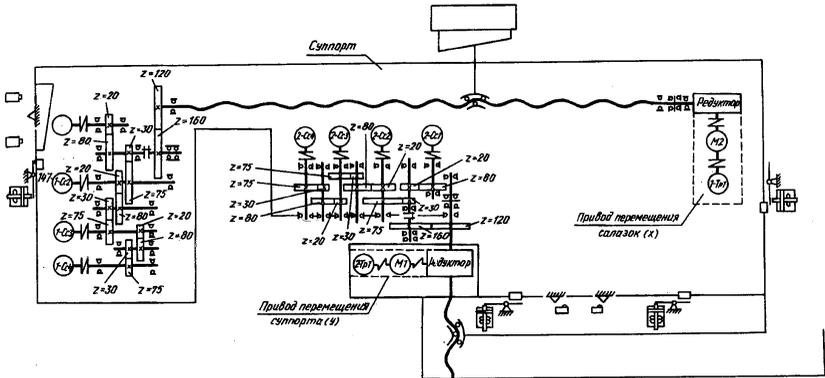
Кинематическая схема привода подачи суппорта многооперационного станка мод. МС12-250М1
